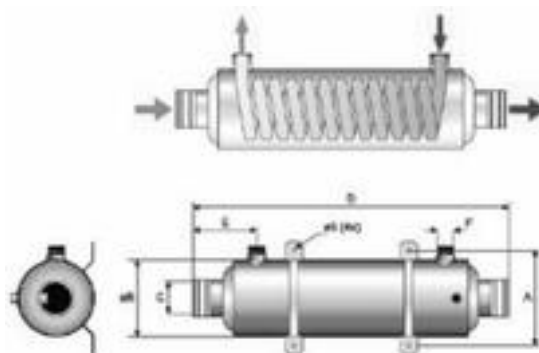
Схема устройства водонагревателя для бассейнов
